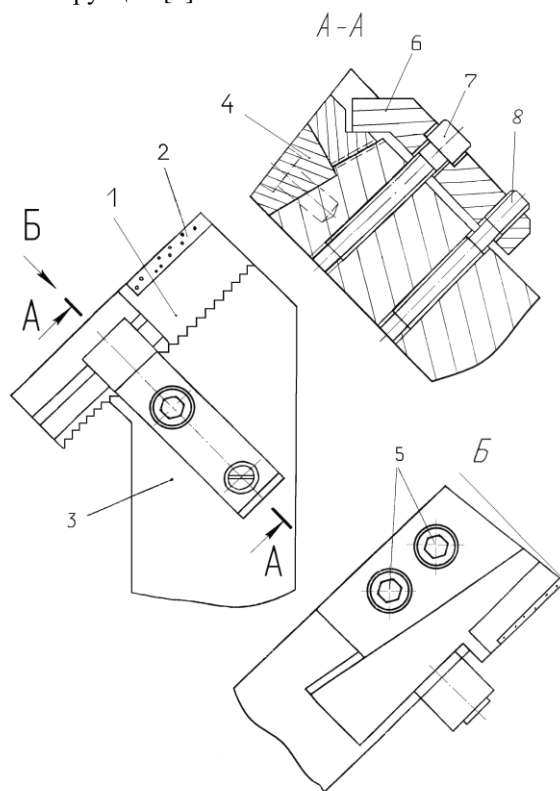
Сборный проходной резец с разрезом А-А и видом Б: 1 – блок; 2 – режущая пластина; 3 – державка; 4 – опорная пластина; 5 – винт; 6 – прихват; 7 – крепежный винт; 8 – дифференциальный винт
